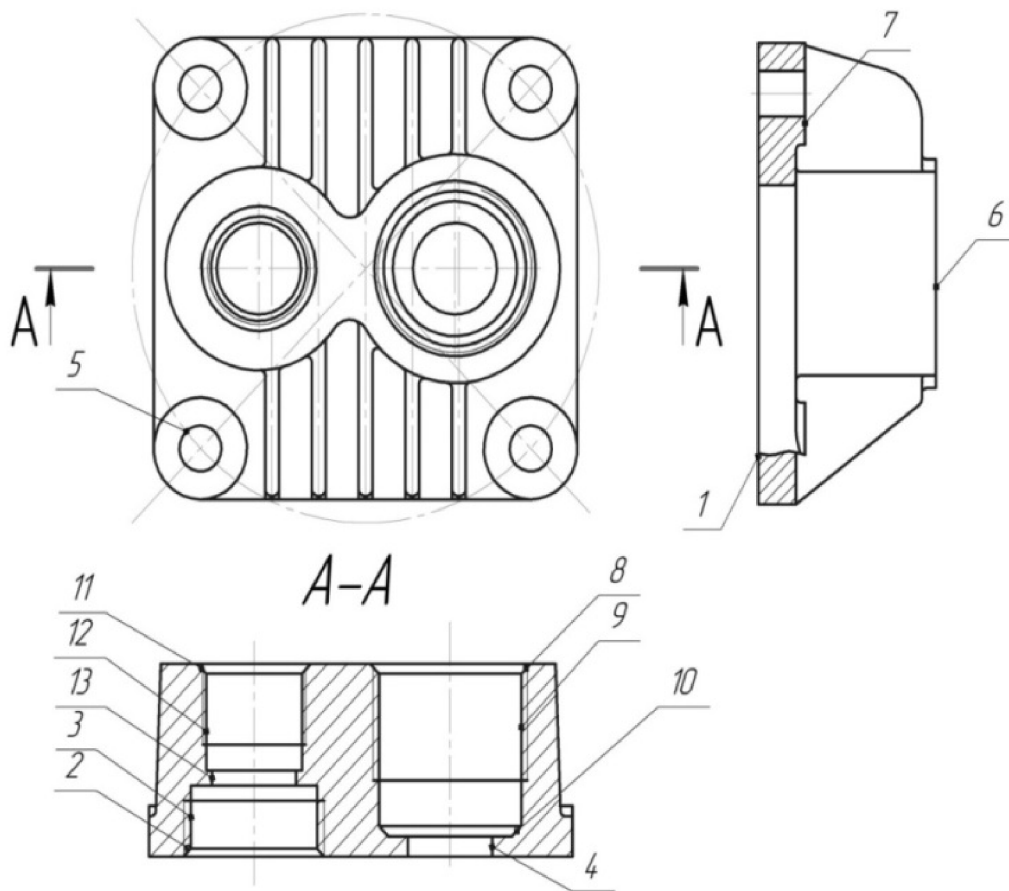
Типова технологічна послідовність обробки поверхонь деталі
